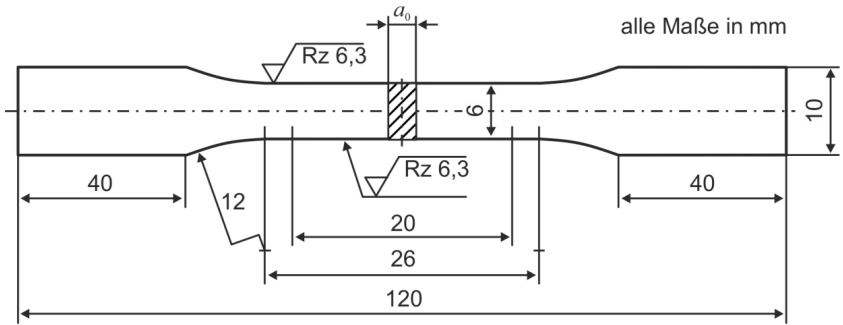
Maße der Zugproben gemäß DIN 50125
